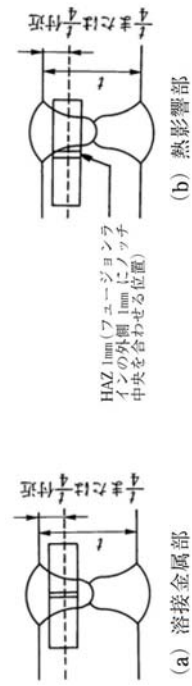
衝撃試験片（開先溶接試験片の採取位置）
